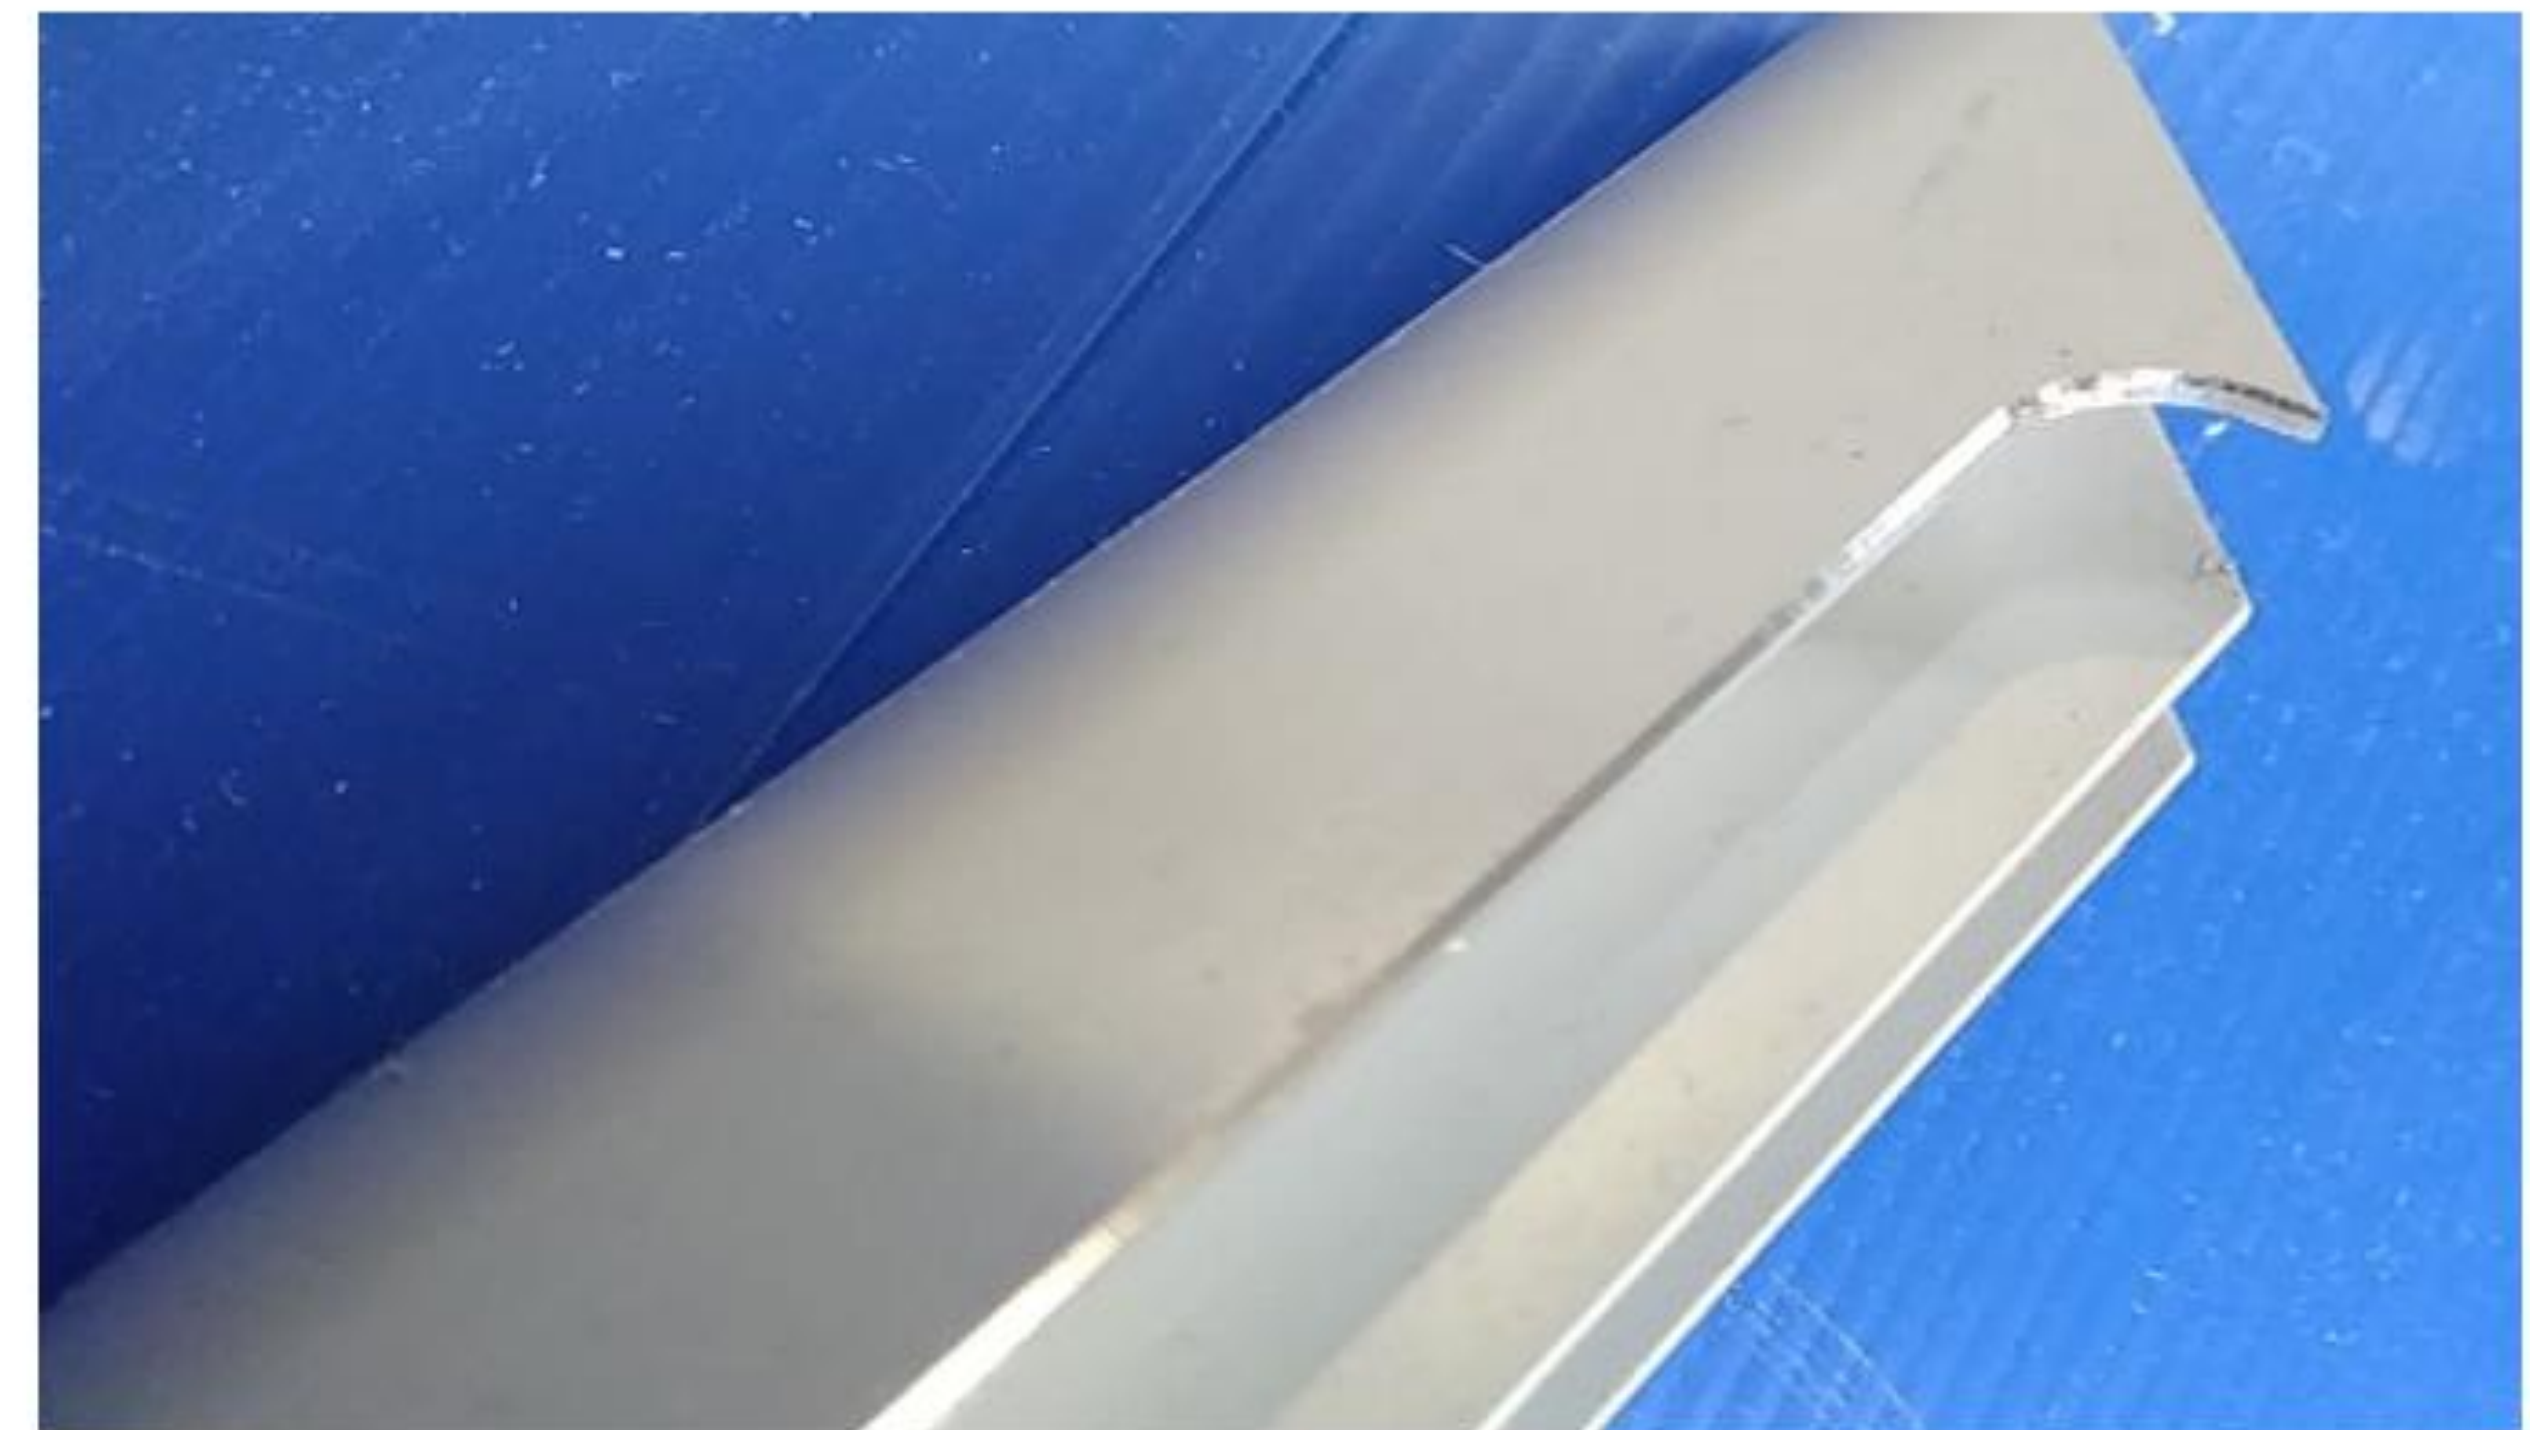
Фаска після оброблення фрезою комбінованою
